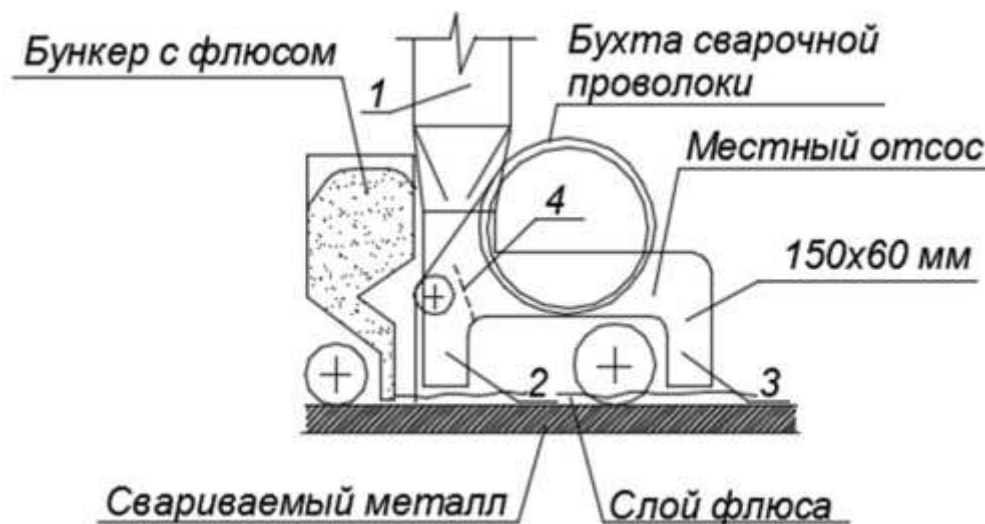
Схема сварочного трактора для сварки под слоем флюса
